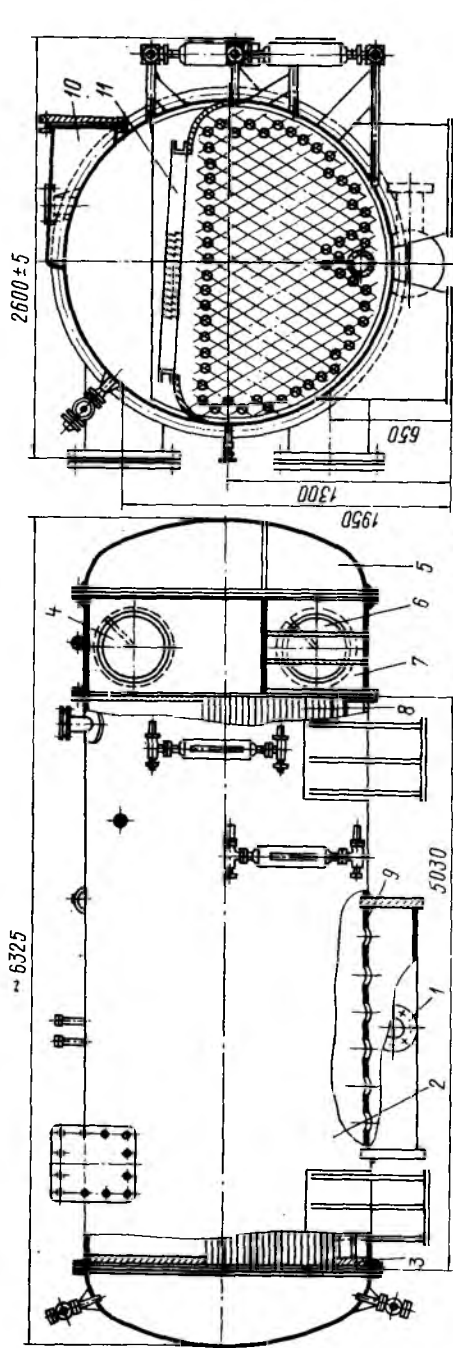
Фреоновый кожухотрубный испаритель затопленного типа для турбокомпрессорного агрегата: 1 — жидкостной коллектор; 2 — обечайка; 3 — трубая решетка; 4, 6 — штуцера для входа и выхода рассола; 5 — крышка; 7 — рассольная камера; 8 — трубы; 9 — распределитель парожидкостной смеси; 10 — выход пара; 11 — сепаратор
